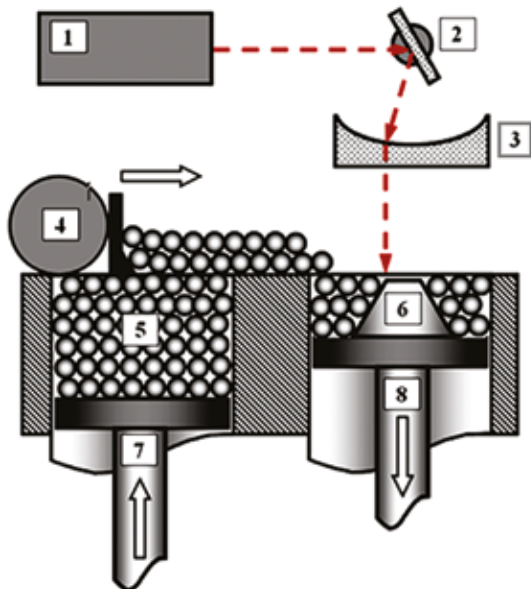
Функциональная схема метода СЛС: 1 — источник лазерного излучения; 2 — система поворота зеркал; 3 — F-Theta-линза; 4 — роликовый скрепер; 5 — используемый порошок; 6 — порошок или изделие; 7 — платформа подачи порошка; 8 — платформа 3D-печати
